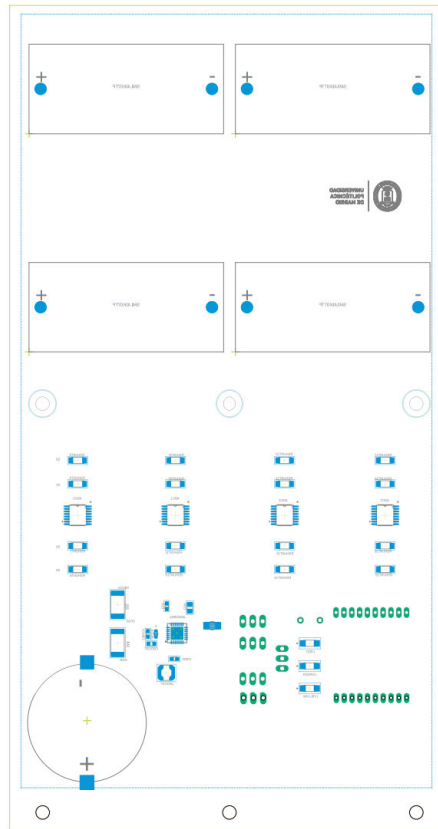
Distribución de Componentes en la PCB – Cara Orientada al Sol
